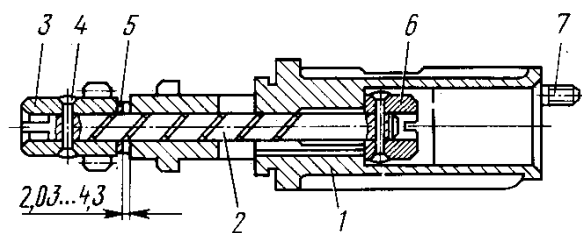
Привод распределителя зажигания: 1 — корпус привода валика распределителя зажигания; 2 — валик привода распределителя зажигания; 3 — шестерня привода распределителя зажигания; 4 — штифт; 5 — упорная шайба; 6 — поводок распределителя; 7 — шпилька
